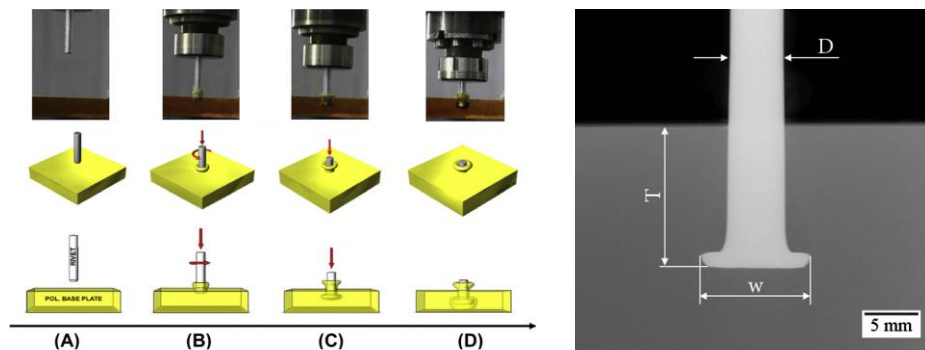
Principe du procédé FricRiveting [78] et vue en coupe d'un joint riveté par rayon X [76]
